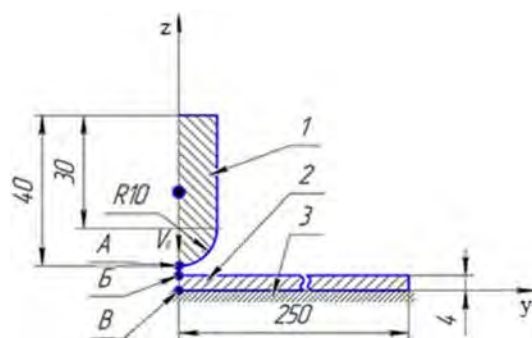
Розрахункова схема процесу динамічного навантаження пластини, що динамічно обробляється: 1 – індентор; 2 – пластинка; 3 – абсолютно жорстка опора, А – точка на зовнішній поверхні індентора, В – точка на зовнішній поверхні пластини, В – точка на тильній поверхні пластини
